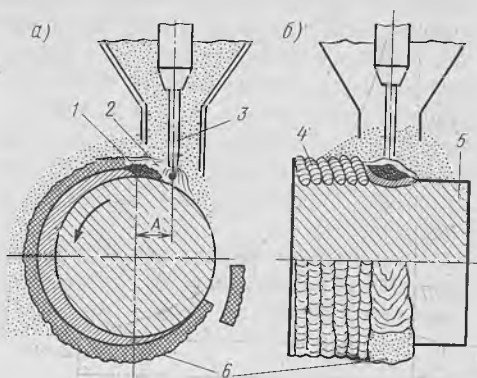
Схема наплавки под слоем флюса: а — поперечный разрез; б — продольный разрез; 1 — ванна расплавленного металла; 2 — расплавленный флюс; 3 — электродная проволока; 4 — наплавленный слой металла; 5 — деталь; 6 — шлаковая корка; А — смещение электродной проволоки с зенита
